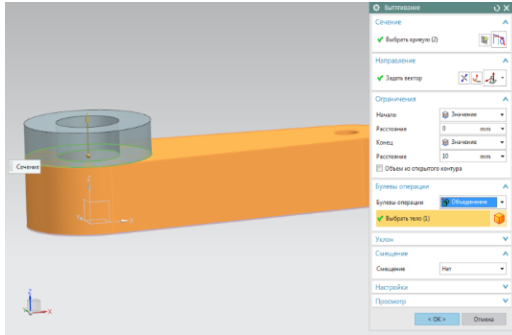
Вытягивание эскиза на верхней поверхности детали
